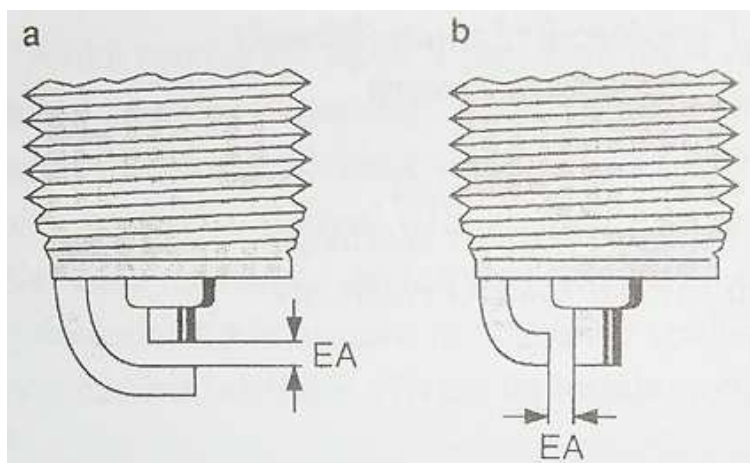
Konstrukce zapalovací svíčky [12]
